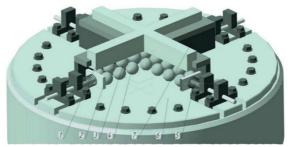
Конструкция буферного устройства с двумя передаточными механизмами: 1 - ползун, 2 - упор, 3 - верхние шарики, 4 - нижние шарики, 5 - пружина, 6 - корпус, 7 - боковые направляющие
